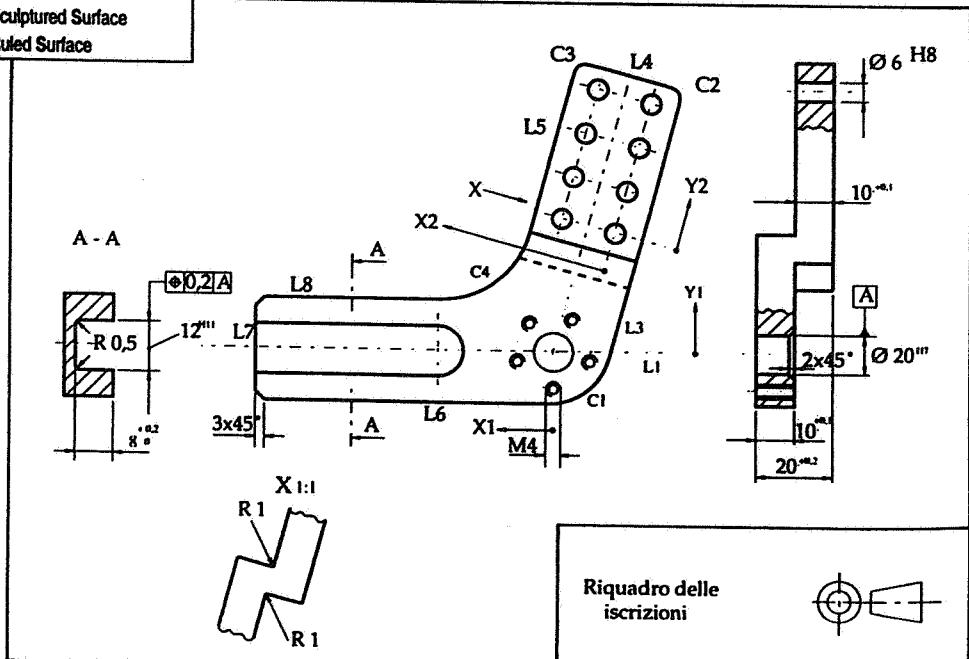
Quotatura con indicazione di tolleranze e dimensioni per diverse lavorazioni.
